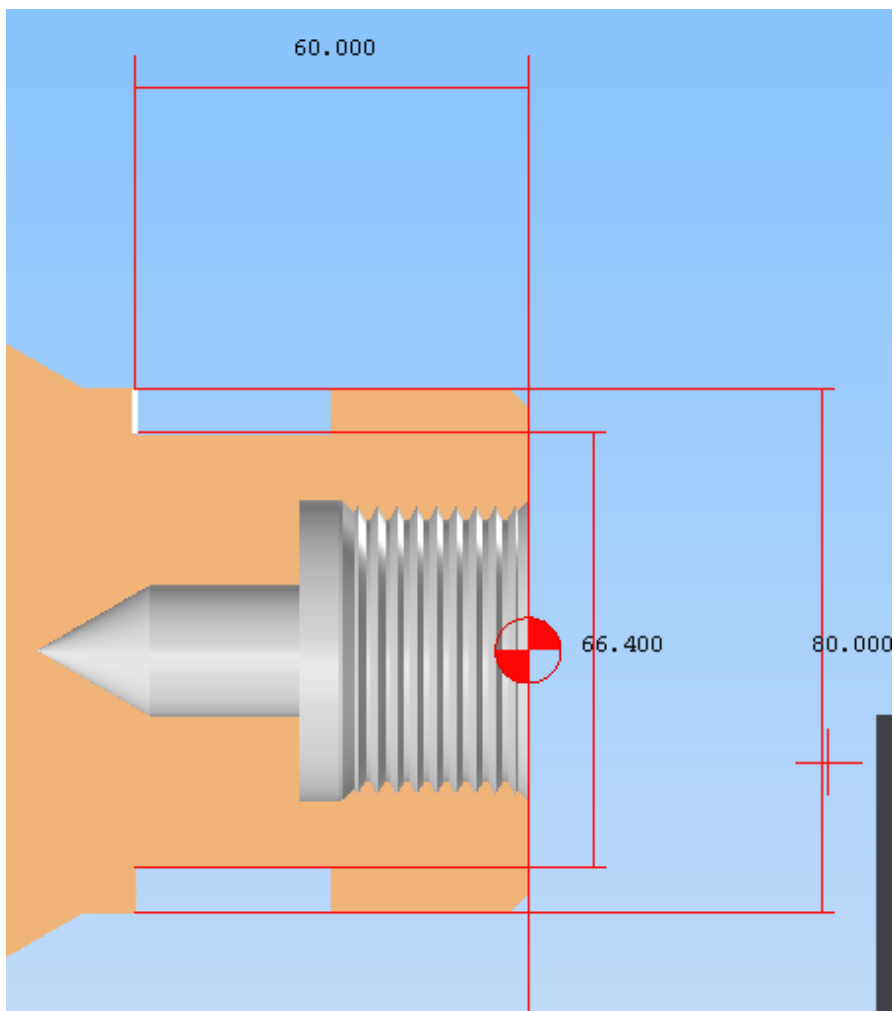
Контроль лінійних розмірів канавки після оброблення
